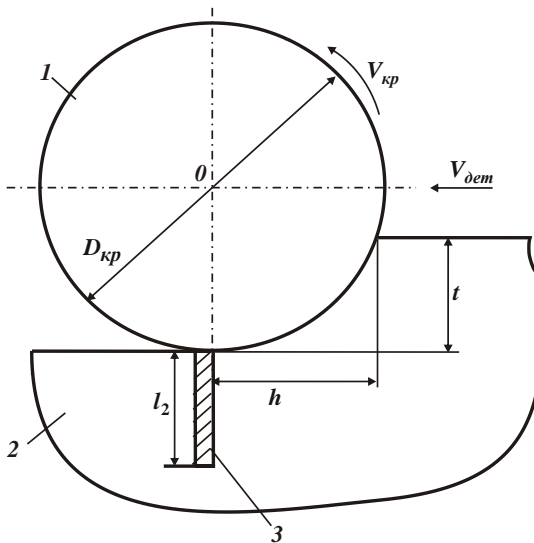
Розрахункова схема плоского шліфування: 1 – круг; 2 – оброблювана деталь; 3 – адіабатичний стержень поверхневого шару деталі
